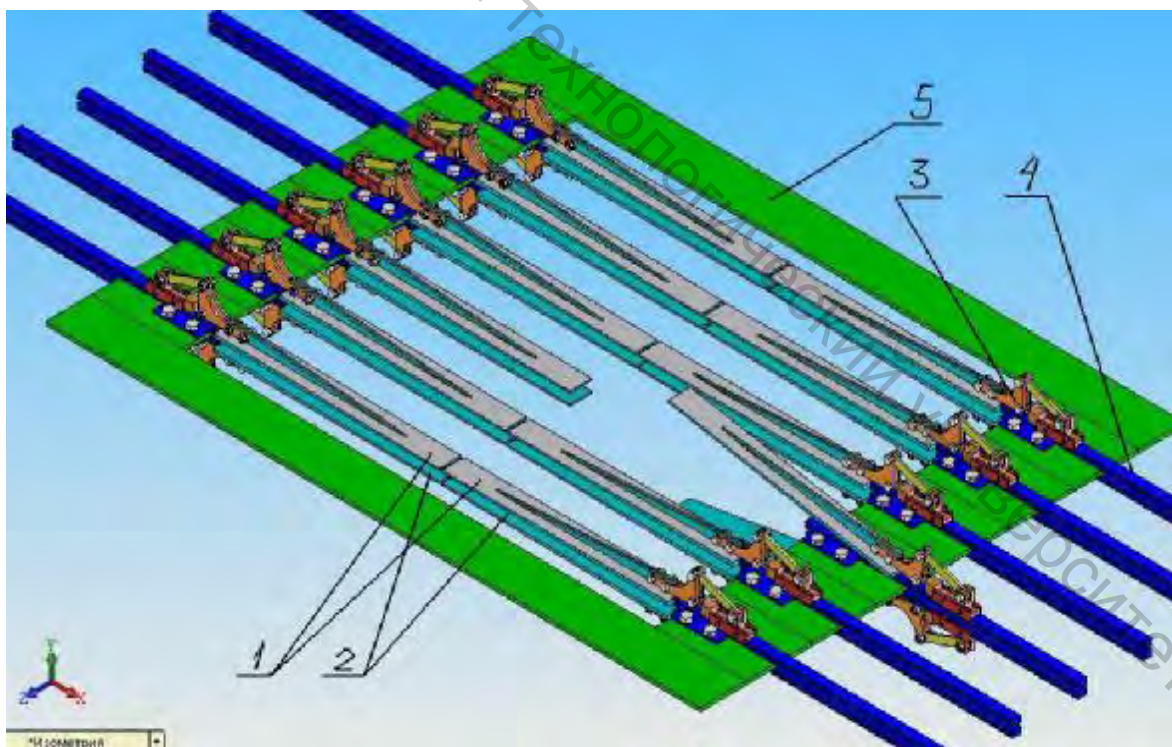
Общий вид устройства фиксации деталей обуви
